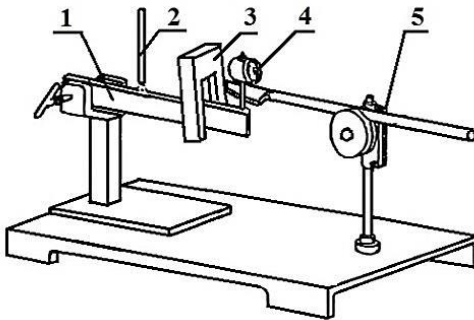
Установка для вимірювання деформацій у процесі зварювання чи наплавлення та охолодження де: 1– пластина (зразок), що нагрівається; 2 – електрод; 3 – захисний екран; 4 – індикатор годинникового типу; 5 – штатив
